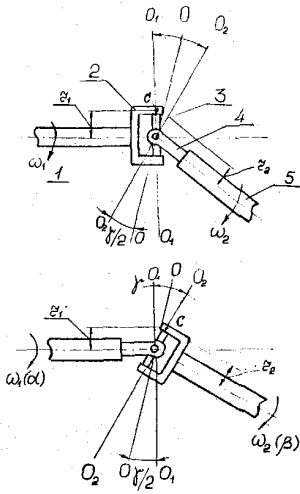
Схема роботи карданного шарніра нерівних швидкостей: 1 – вівідний вал; 2 – вилка ведучого вала; 3 – хрестовина; 4 – вилка веденого вала; 5 – ведений вал; r_1 , r_2 – радіуси точки C_1 відносно осей валів 1 і 5; w_1 , w_2 – кутові швидкості ведучого і веденого валів
